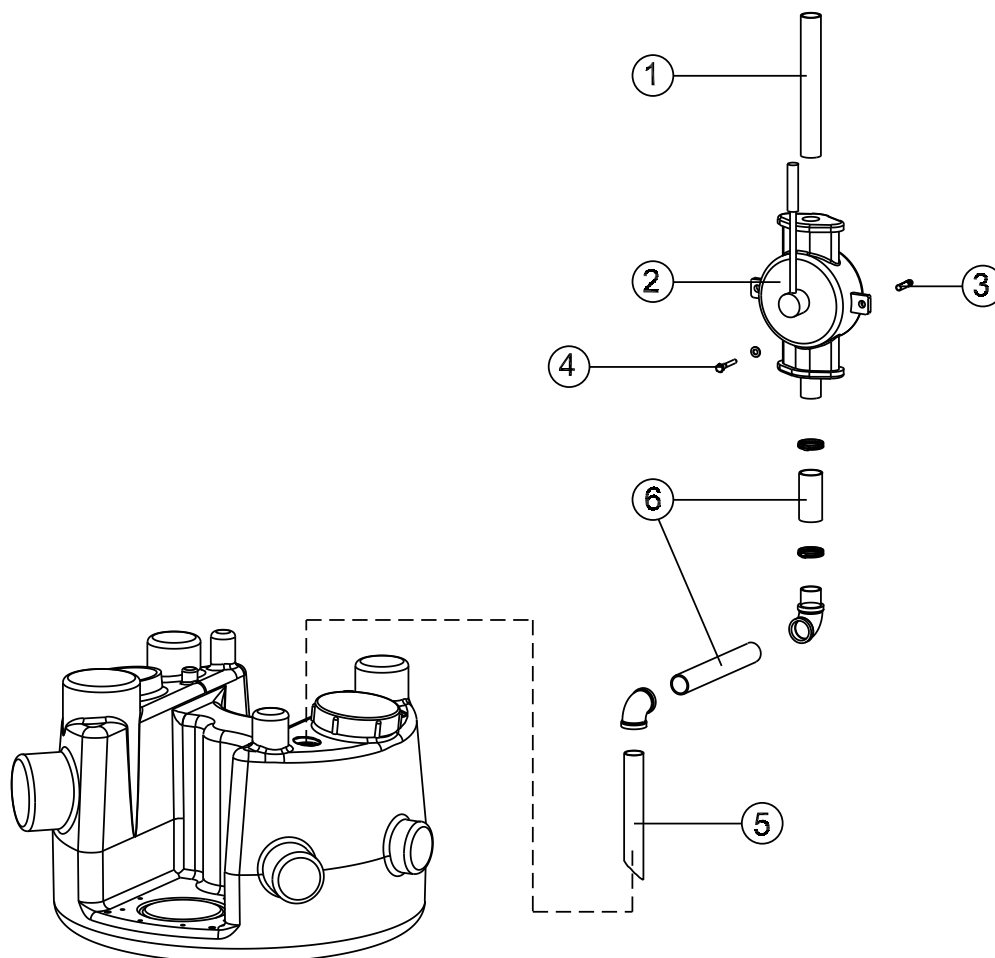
Instalacja zaworu odcinającego i tulei z kołnierzem
